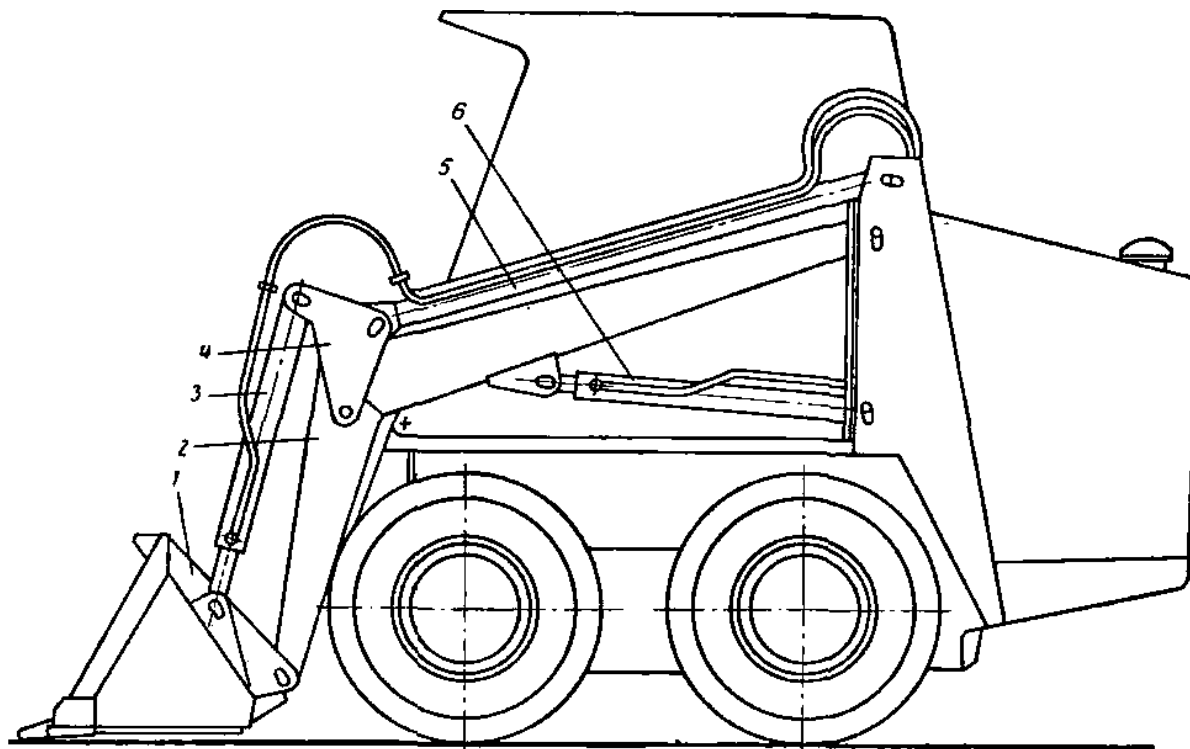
Малогабаритная землеройно-транспортная машина ТО-31:
